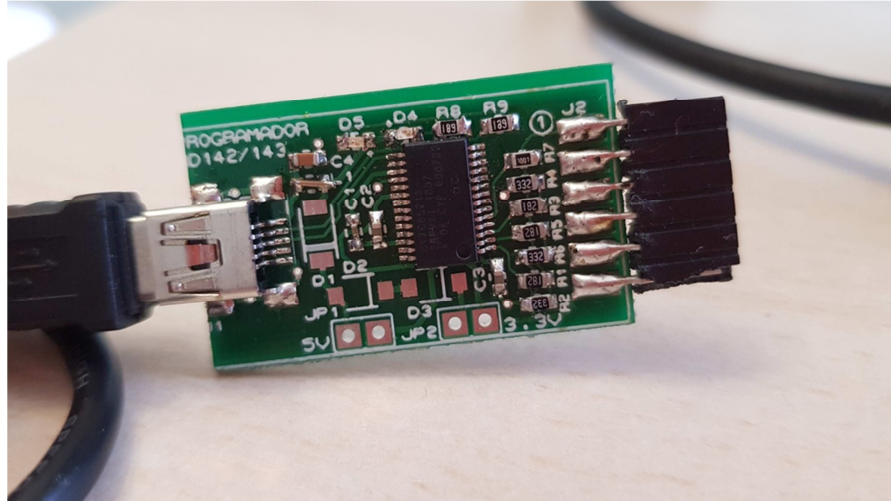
PCB conversor USB-serie con los componentes soldados.
